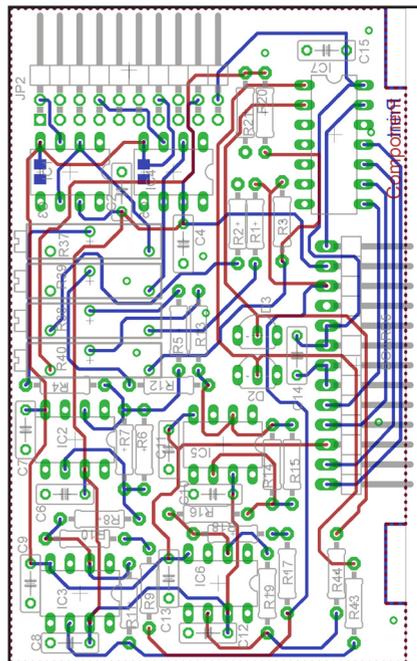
Das Layout der AD-Wandler- Baugruppe 5
